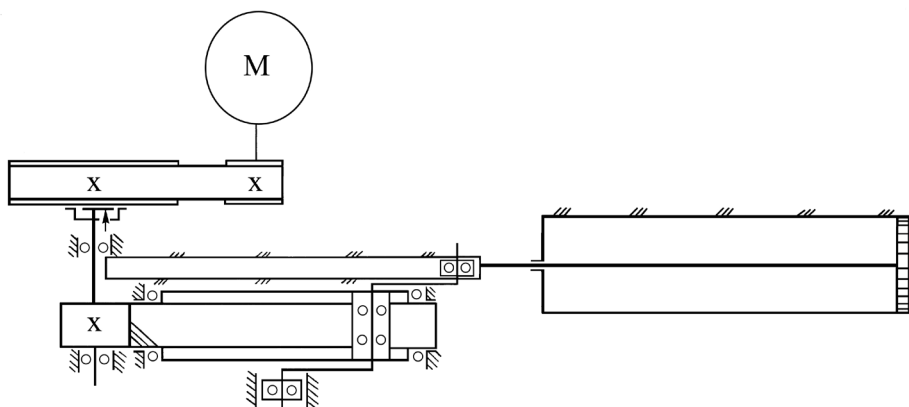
Кинематическая схема привода насосной установки НПМ-32/32
